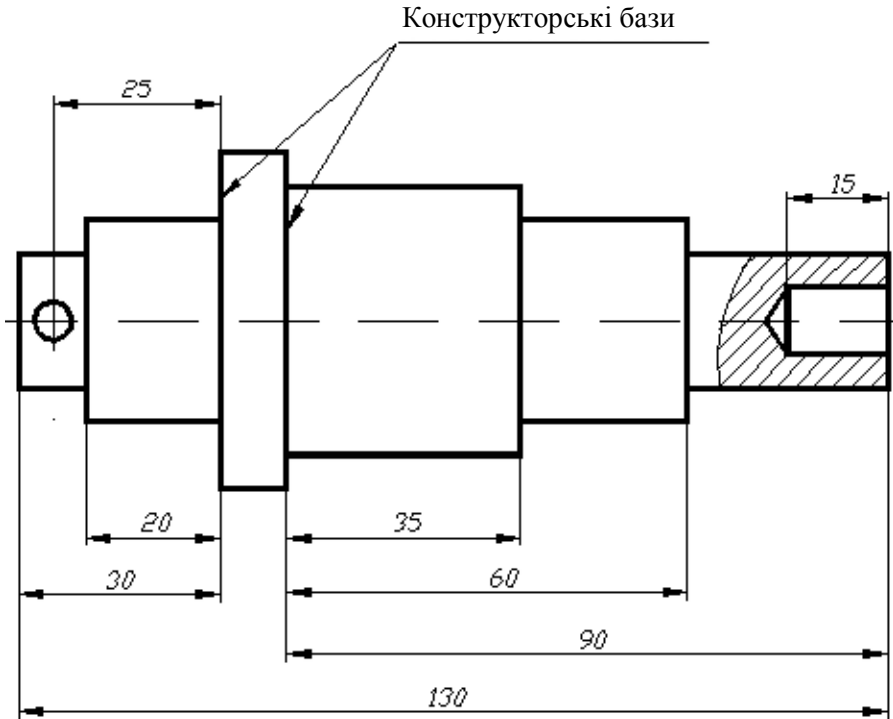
Нанесення розмірів від конструкторських баз
